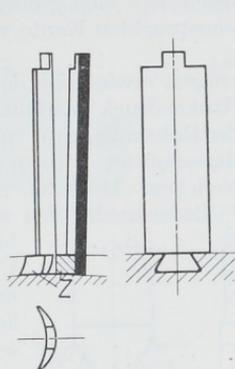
Schaufelbefestigung mittels Schwalbenschwanzes.
